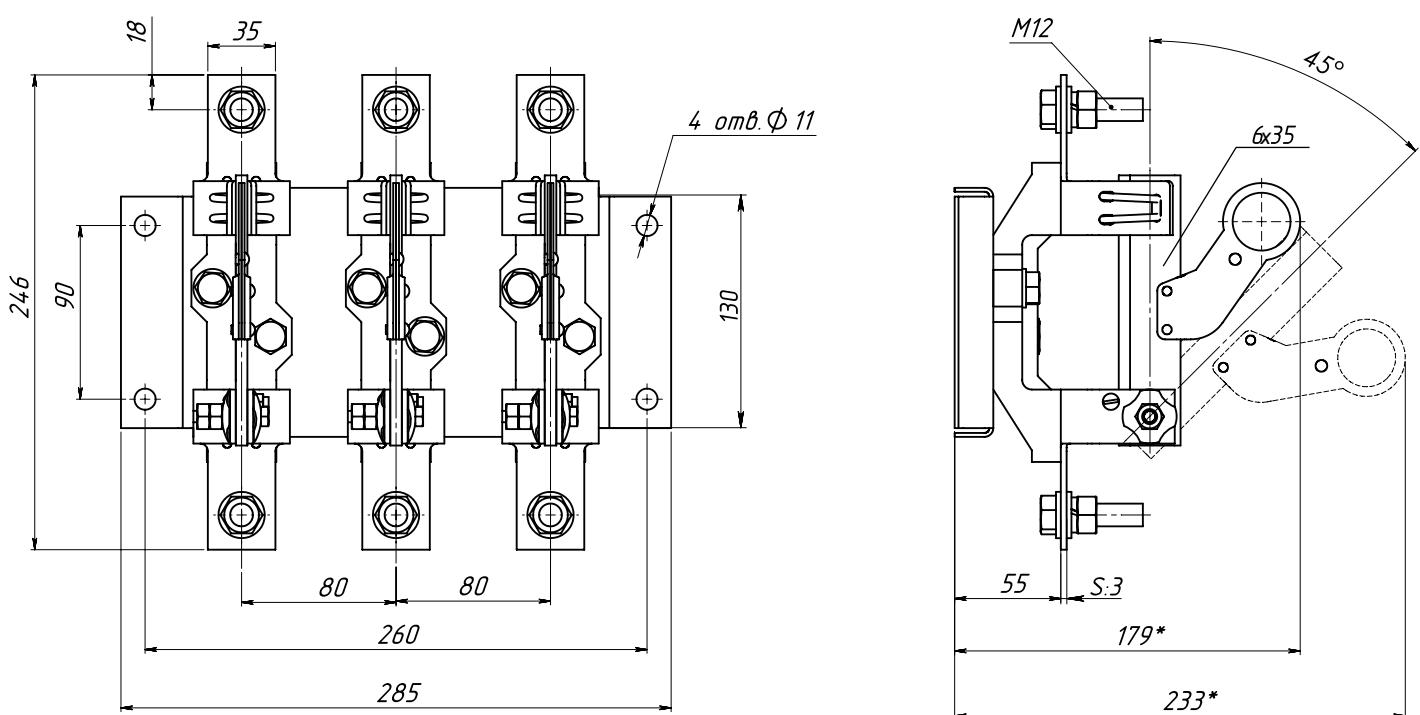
Разъединитель Р63 с пополюсным оперированием штангой ШО-1 на номинальный ток 630 А
